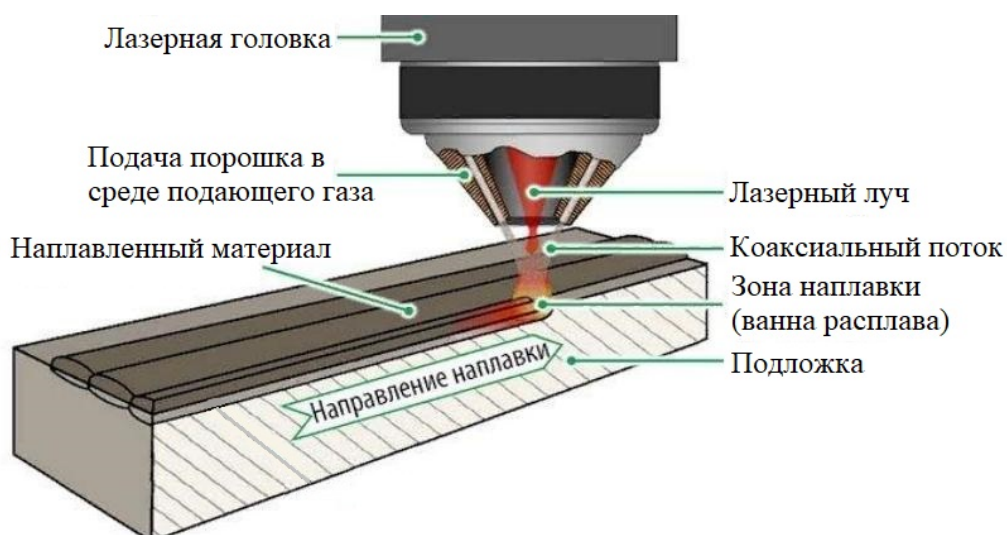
Схема процесса коаксиальной лазерной наплавки
